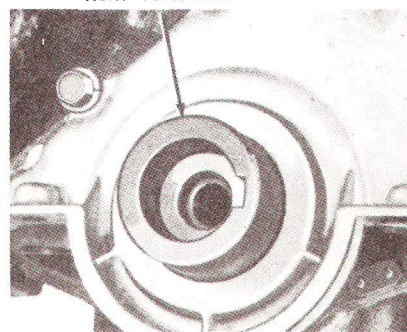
Tapa de Engranajes de Distribución. Típico
